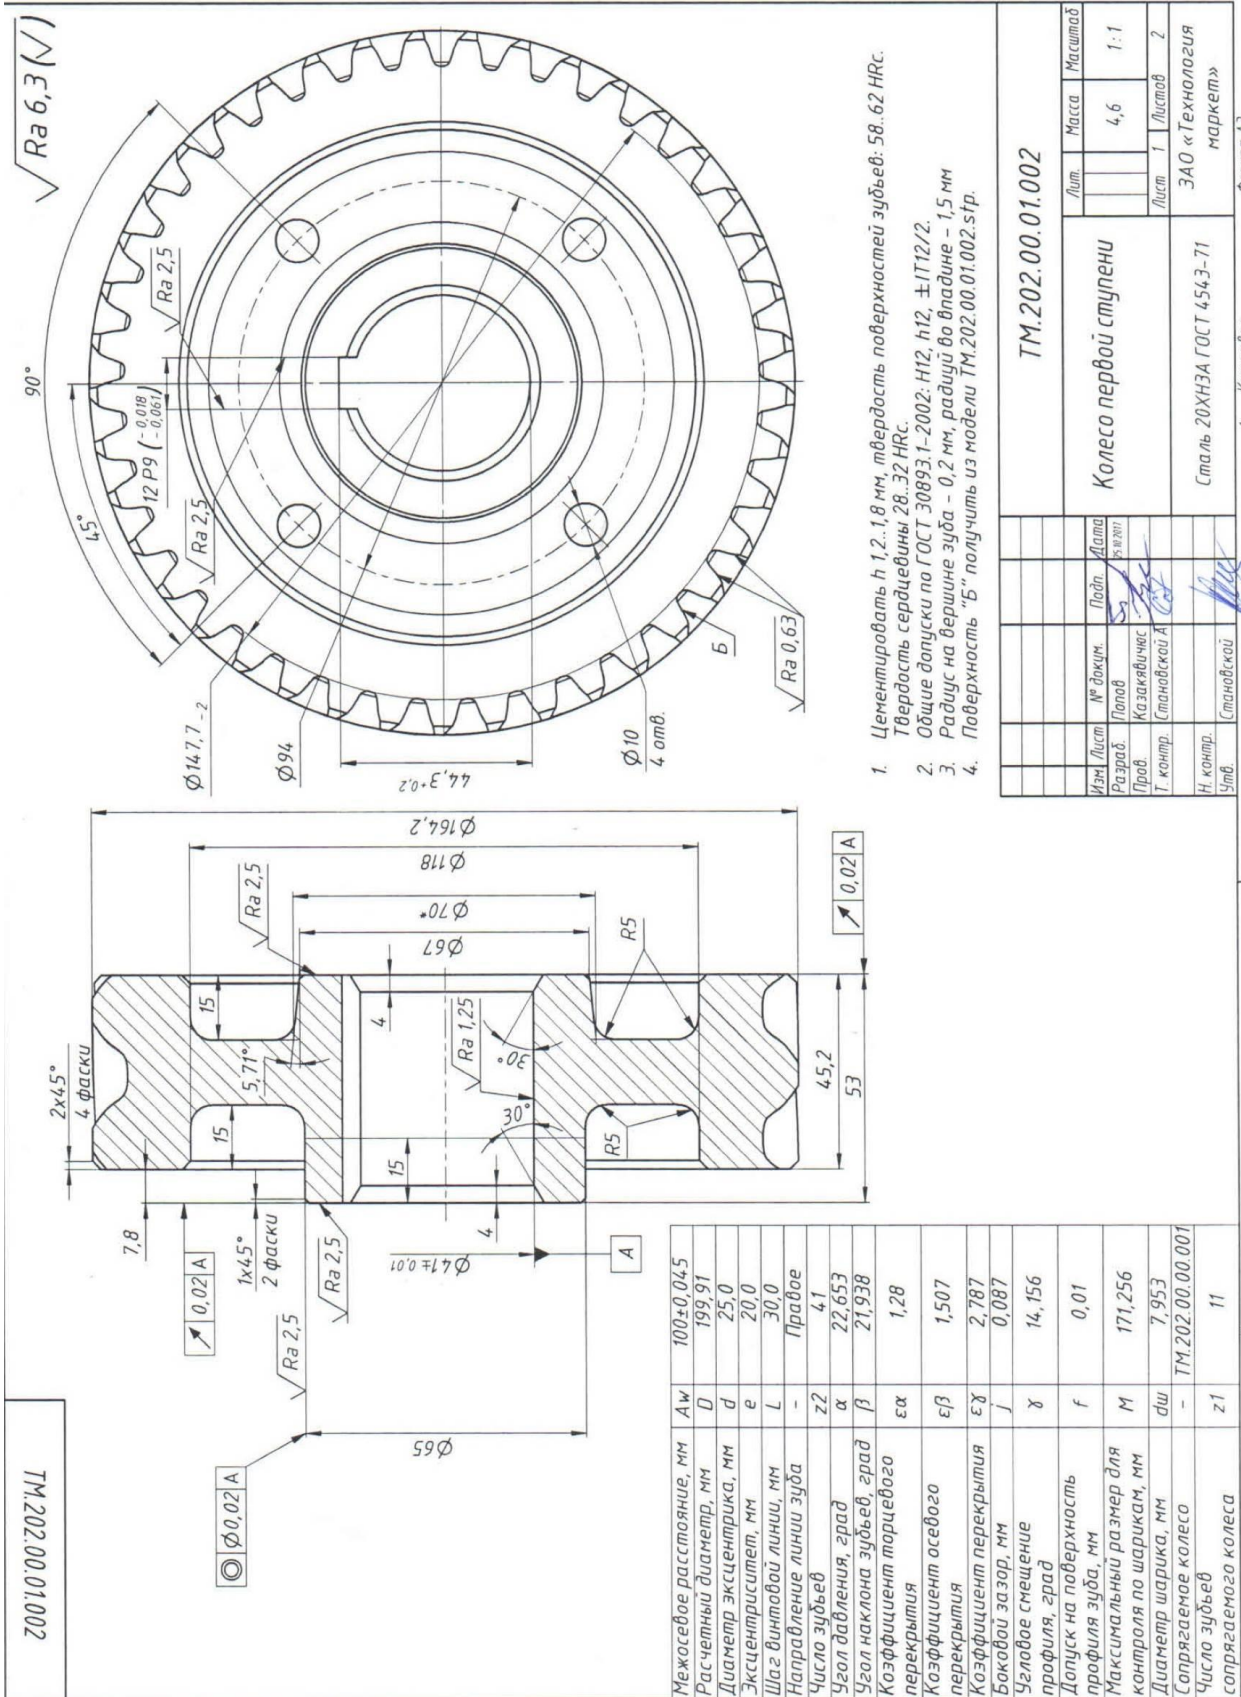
Чертеж колеса первой ступени редуктора с ЭЦ зубчатым зацеплением
